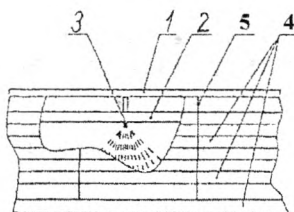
Штанга опрыскивателя с ветрозащитными устройствами:
